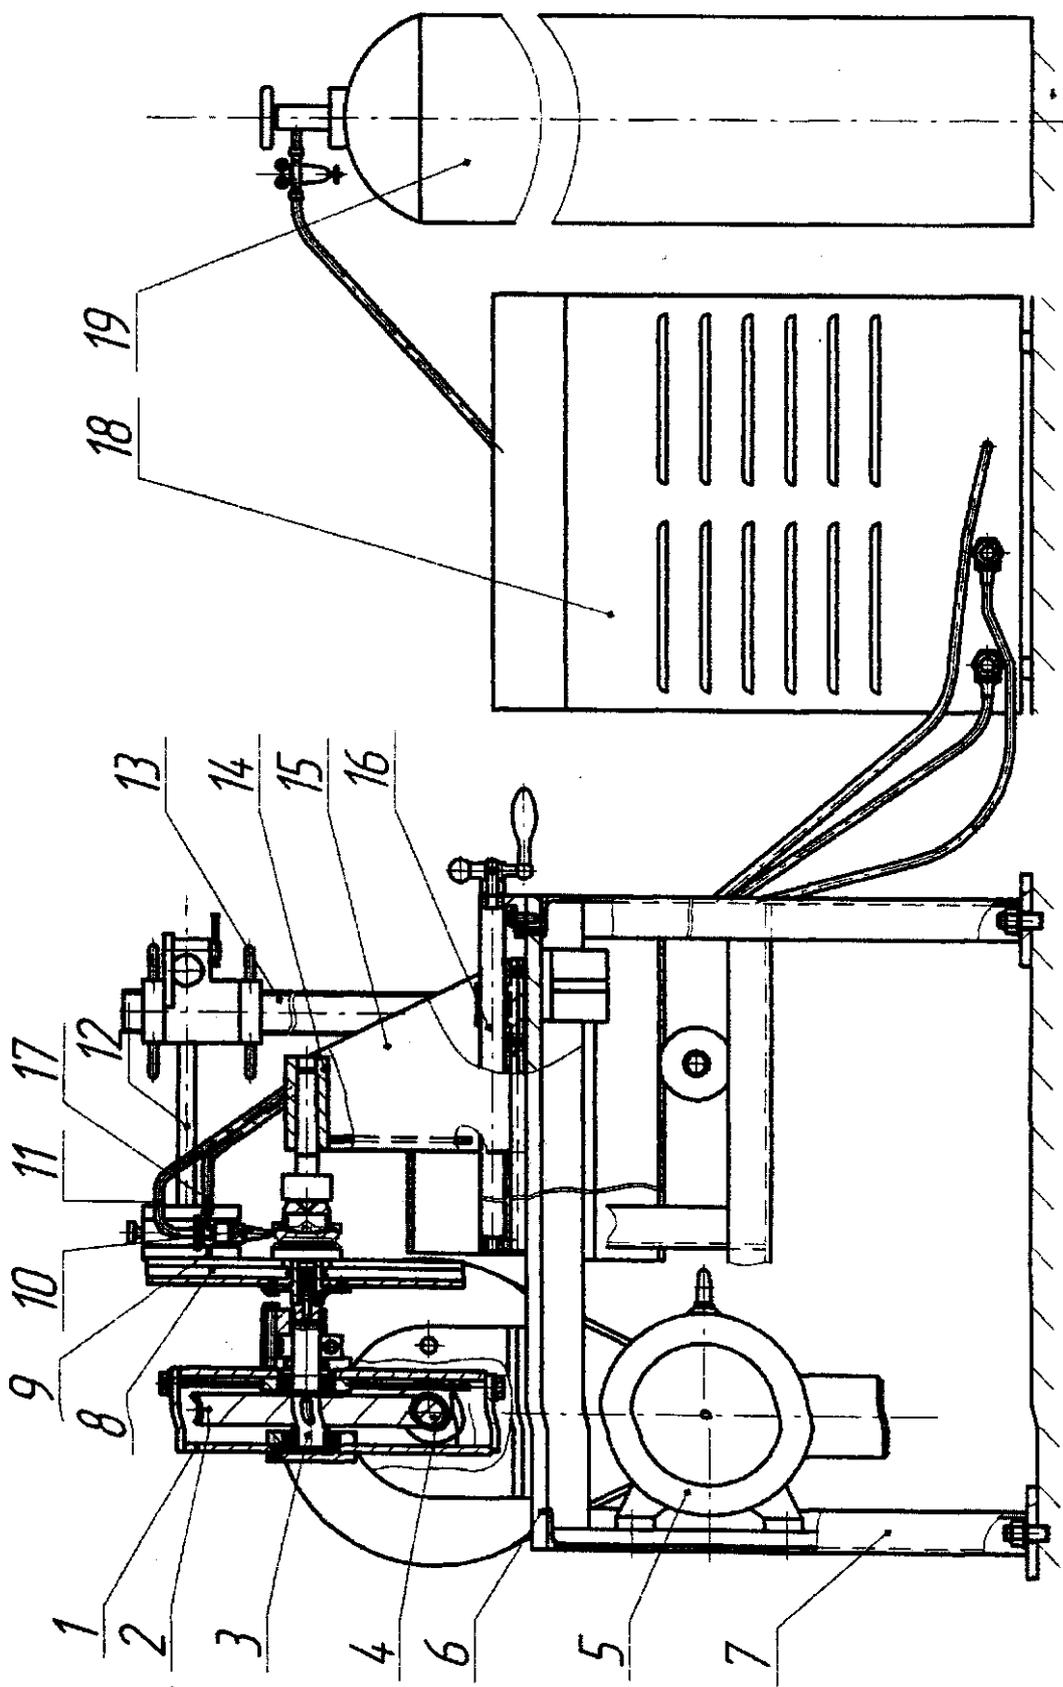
Установка для аргонодуговой сварки кольцевых швов
